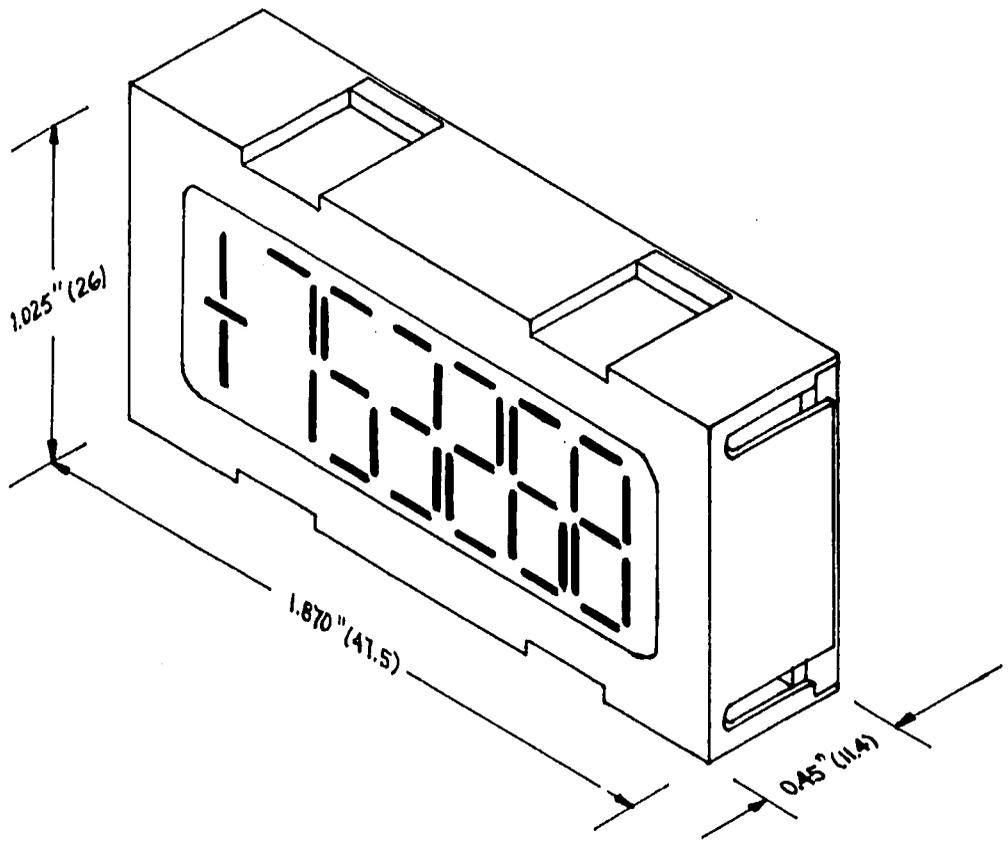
DIMENSIONES DEL CIRCUITO SUPER SUB CUB.
